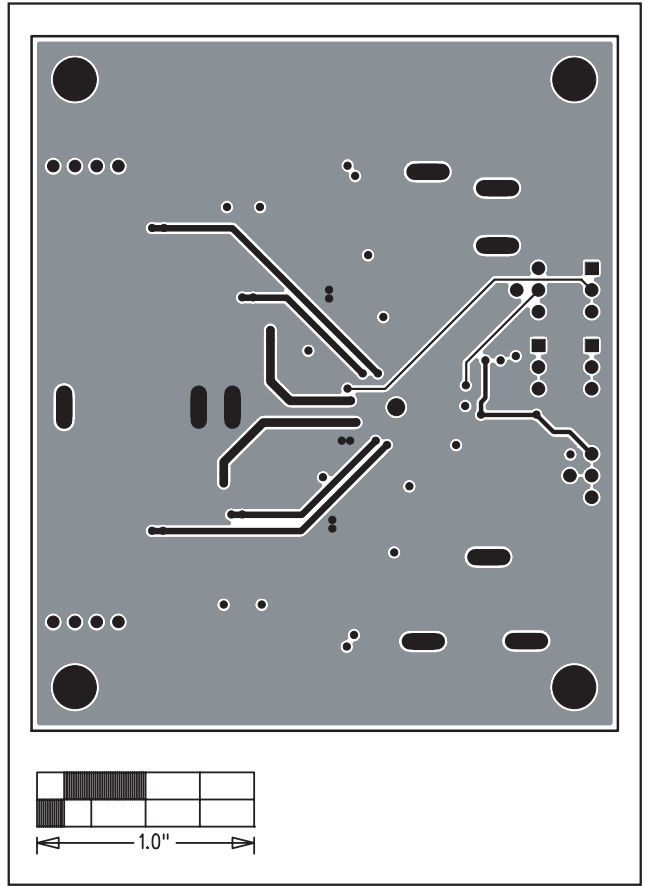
MAX1540 评估板 PCB 布局 – 接地层 2
